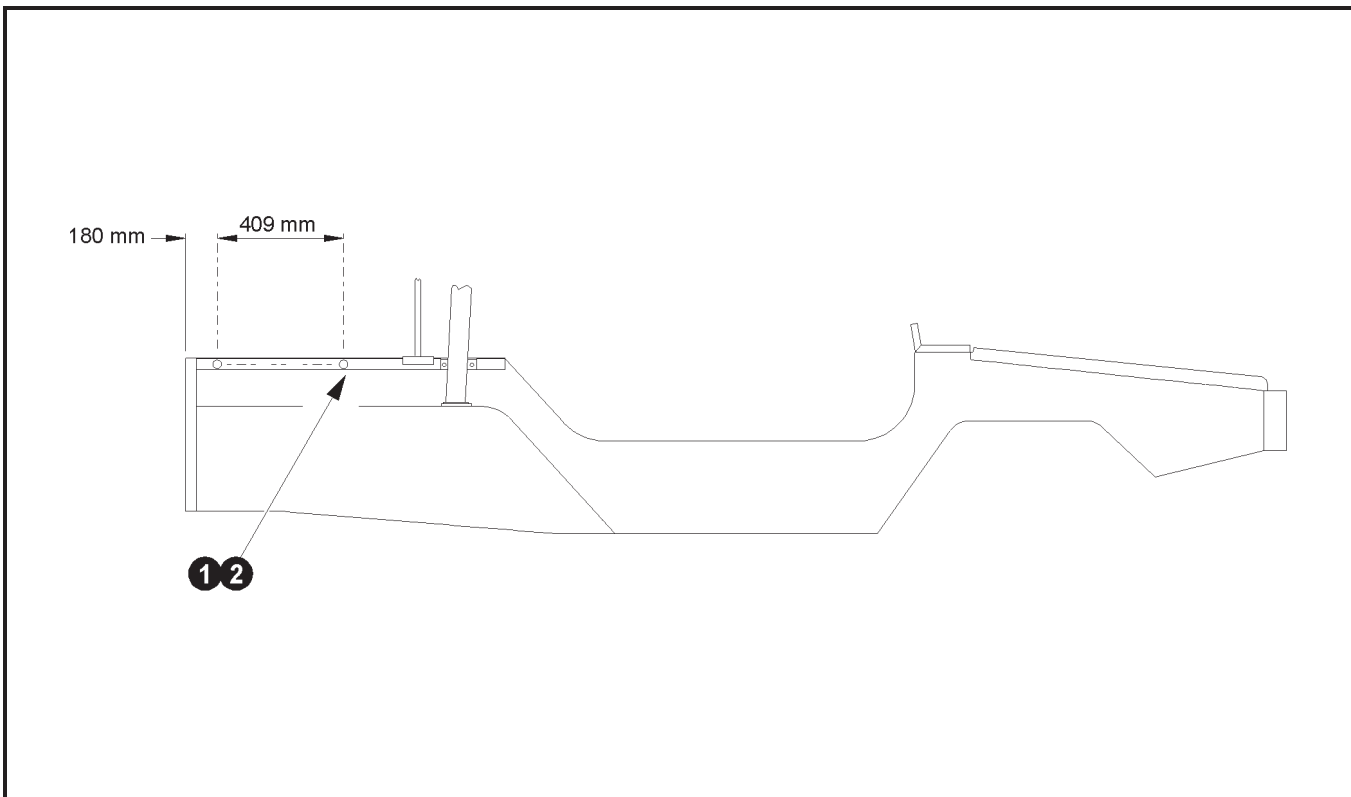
Installation des écrous-rivets aveugles sur le tableau de bord – CA97
